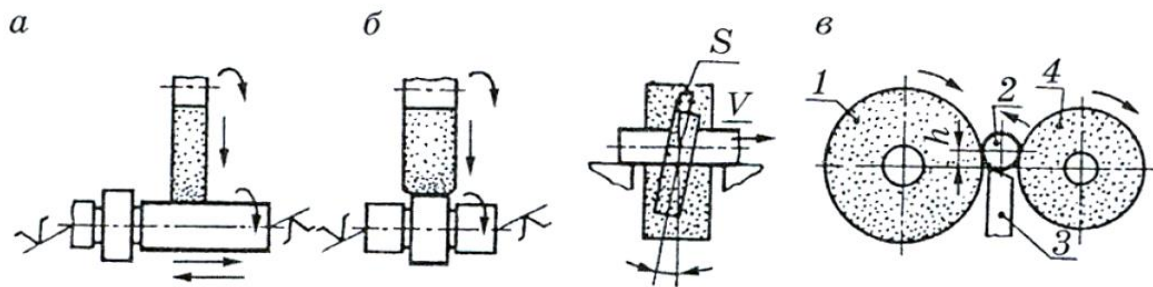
Схемы шлифования валов: 1 – шлифовальный круг; 2 – обрабатываемая заготовка; 3 – нож; 4 – ведущий круг
